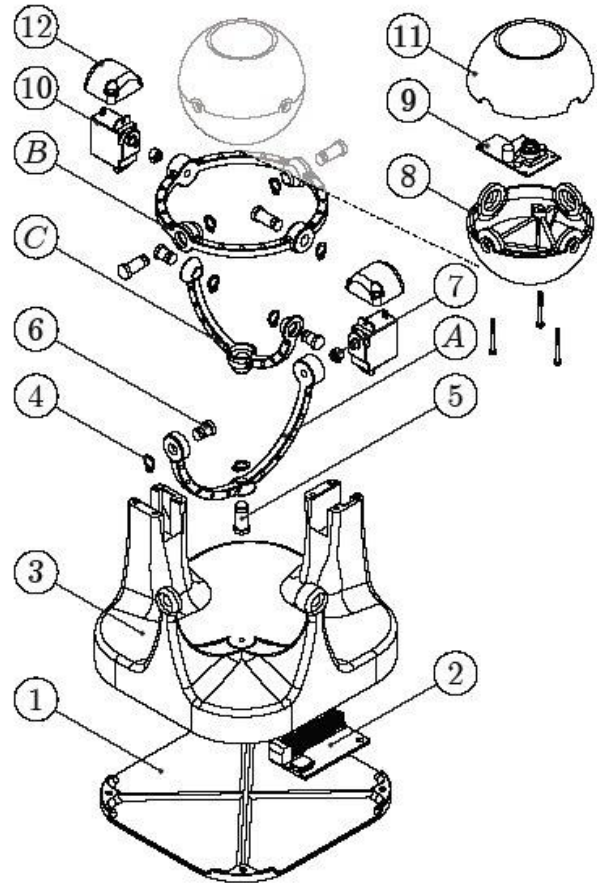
Diseño mecánico del ojo robótico (vista explosiva de componentes).
